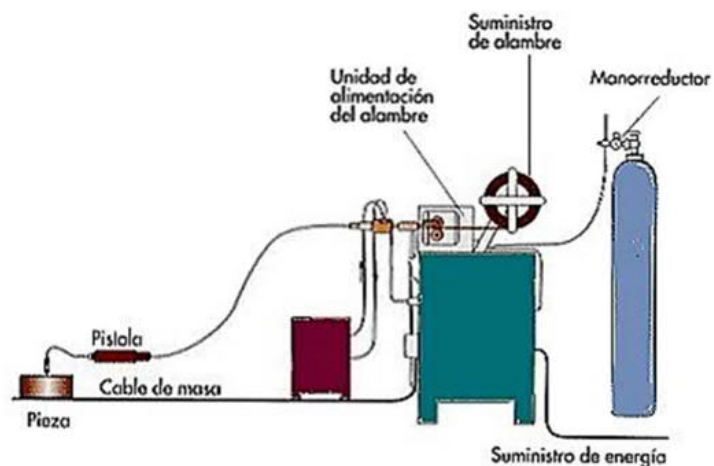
Equipo para el proceso de soldadura GMAW.
